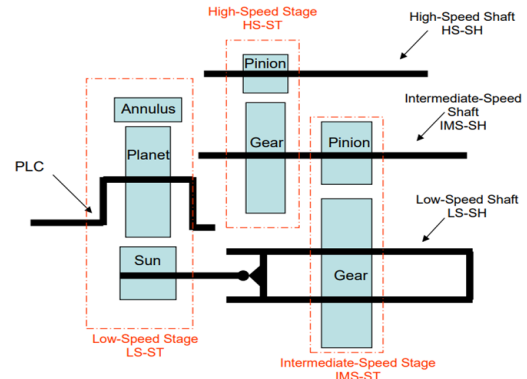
Nomenclatura de la caja de engranajes. Fuente: Sheng (2014)
